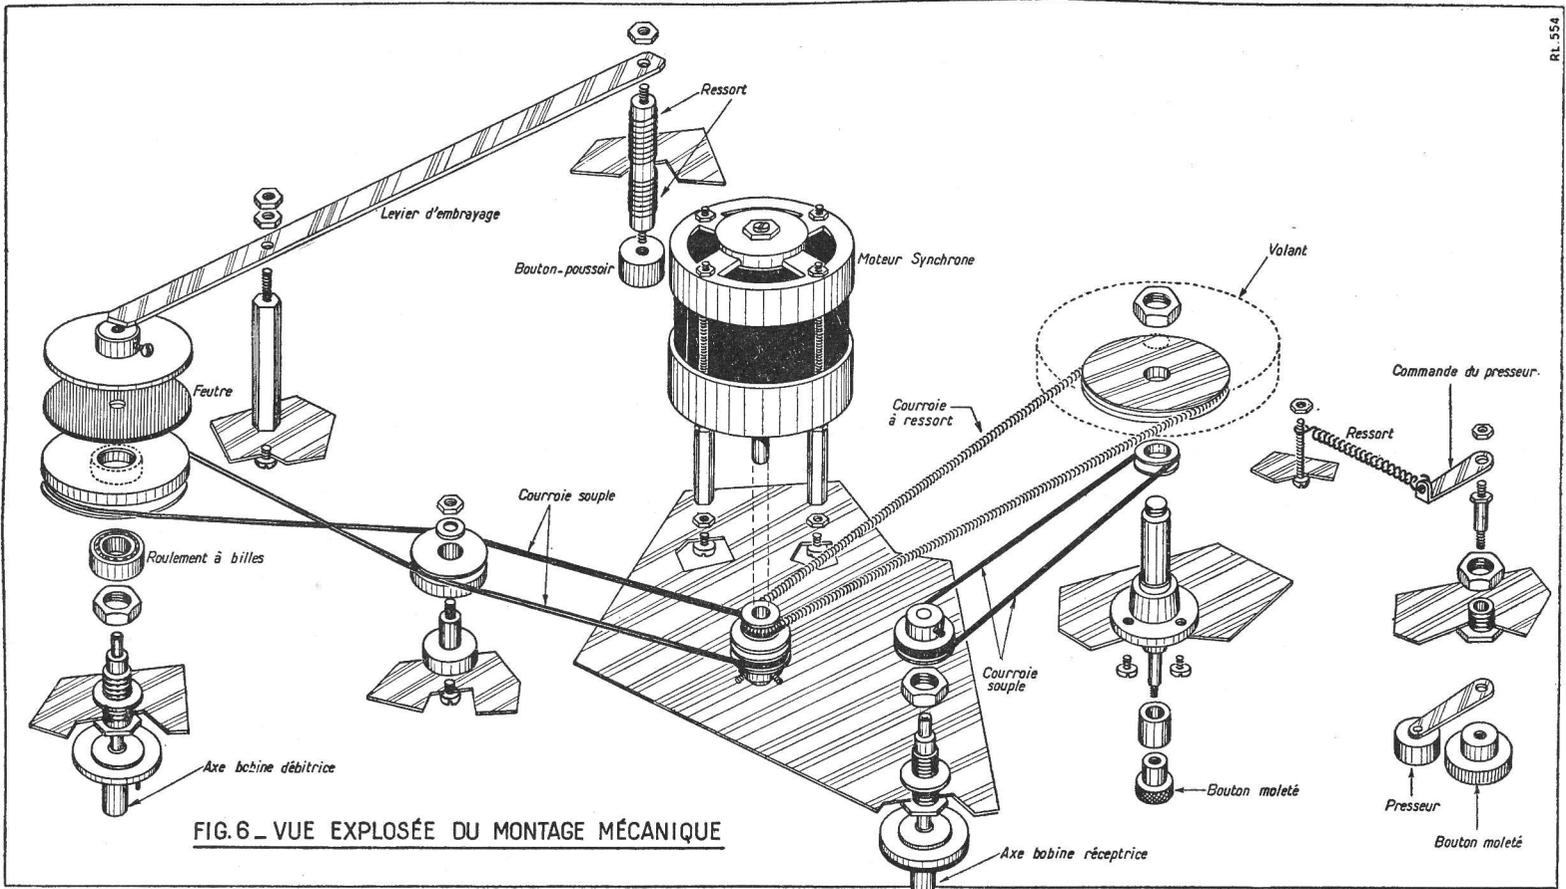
VUE EXPLODÉE DU MONTAGE MÉCANIQUE
